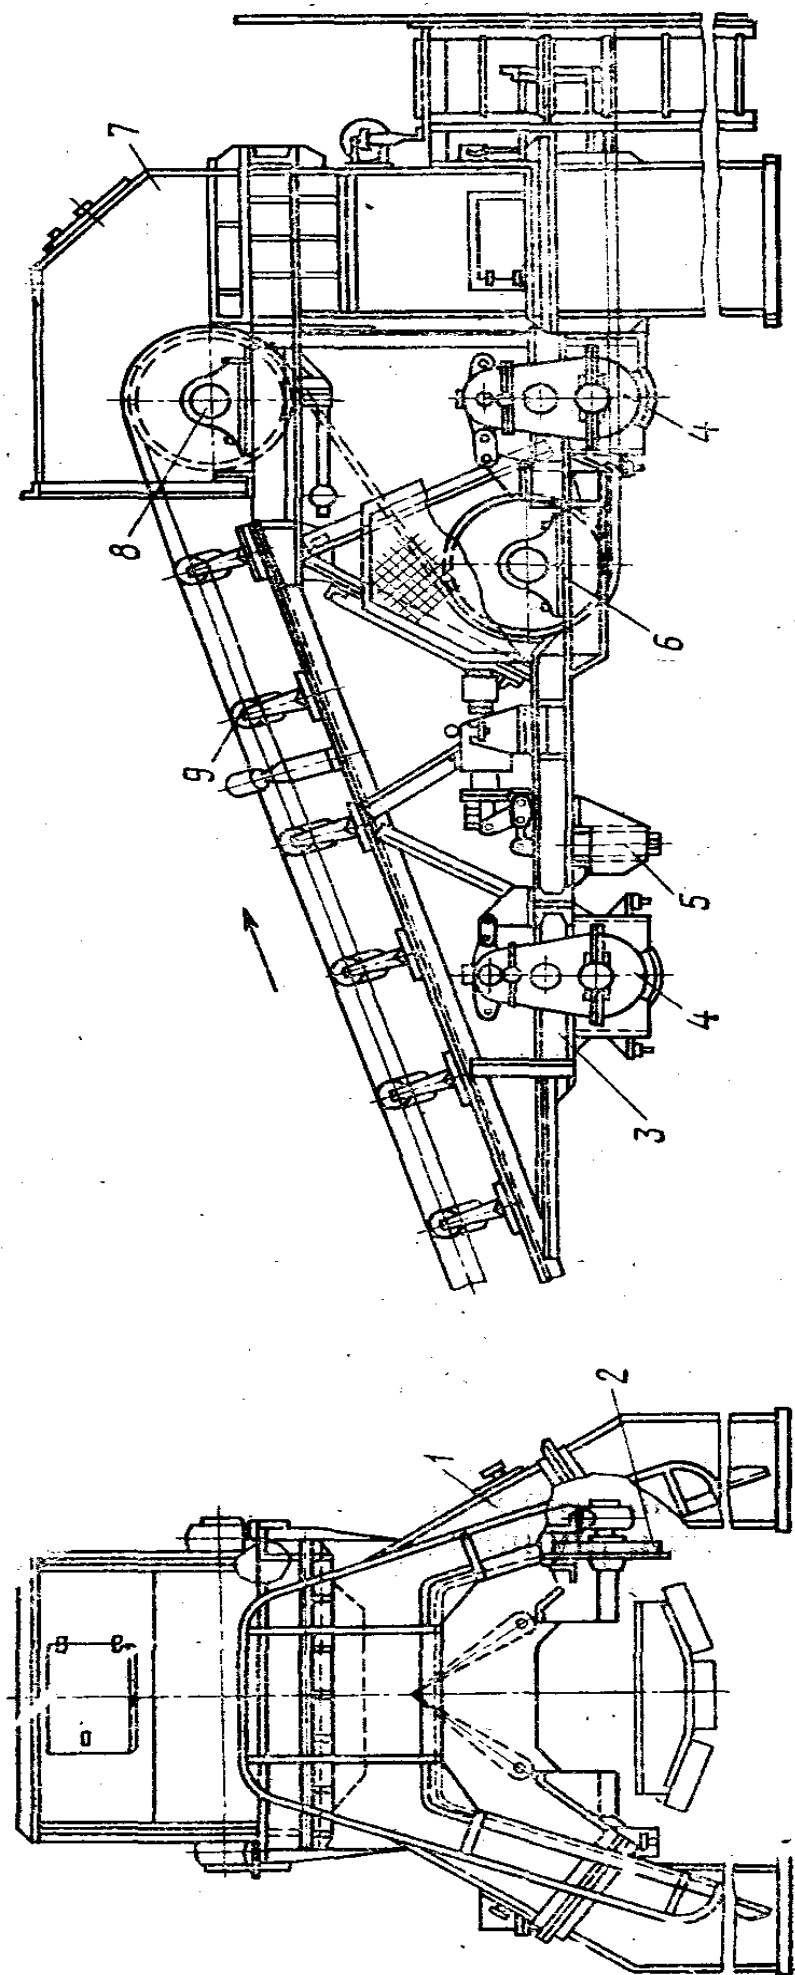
Барабанная разгрузочная тележка с двухрукавной воронкой
